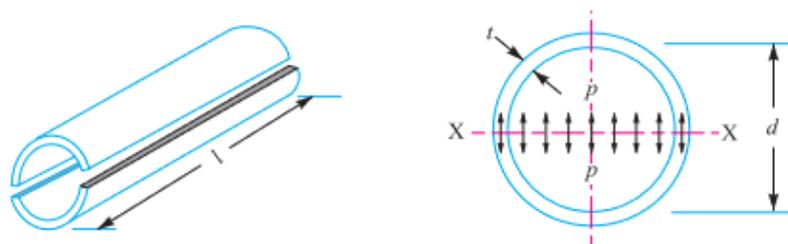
Kegagalan Sepanjang Bagian Longitudinal (Khurmi, 2005)
